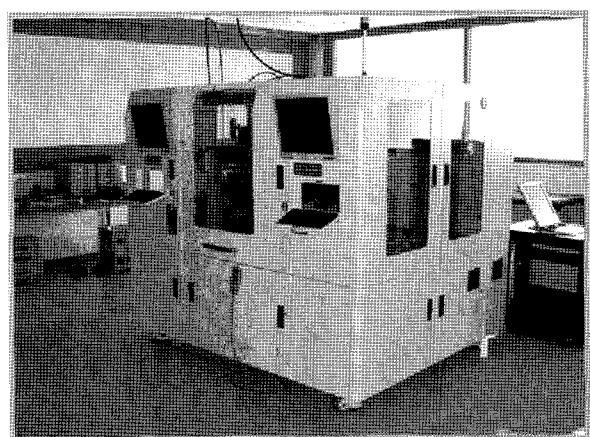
UV Laser Cutting(Sawing) System for SD Card, Usim
